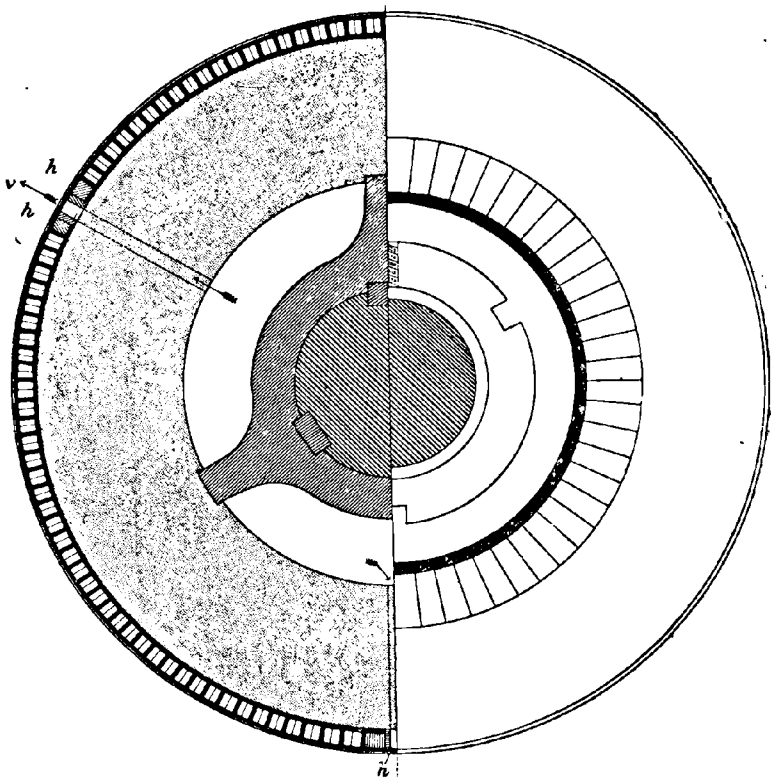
Machine Kapp. — Section d'induit et vue de bout montrant le collecteur.
